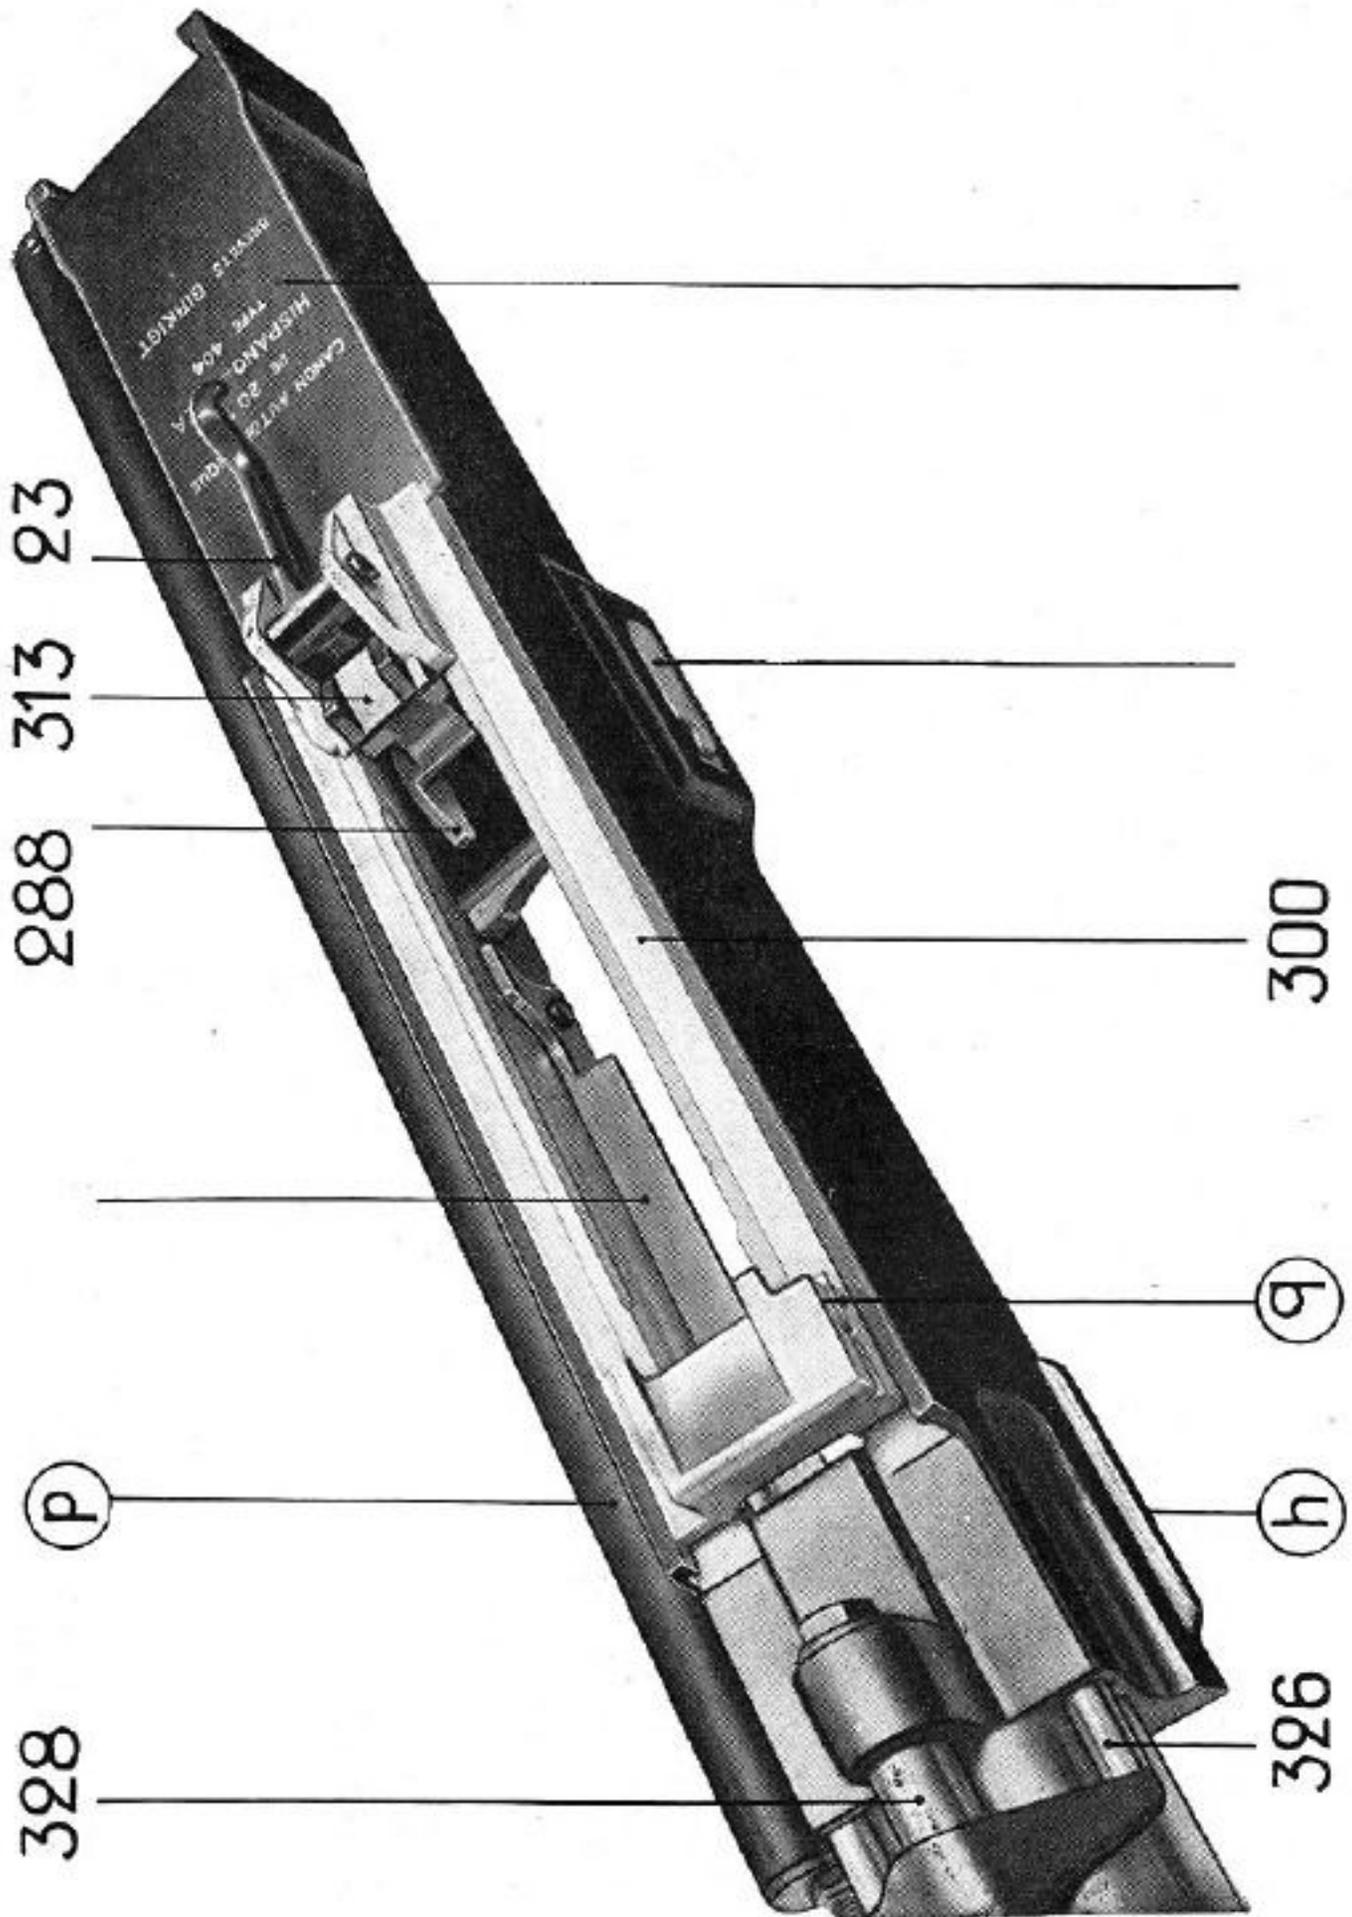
Boîte de culasse et ensemble fixe arrière.
